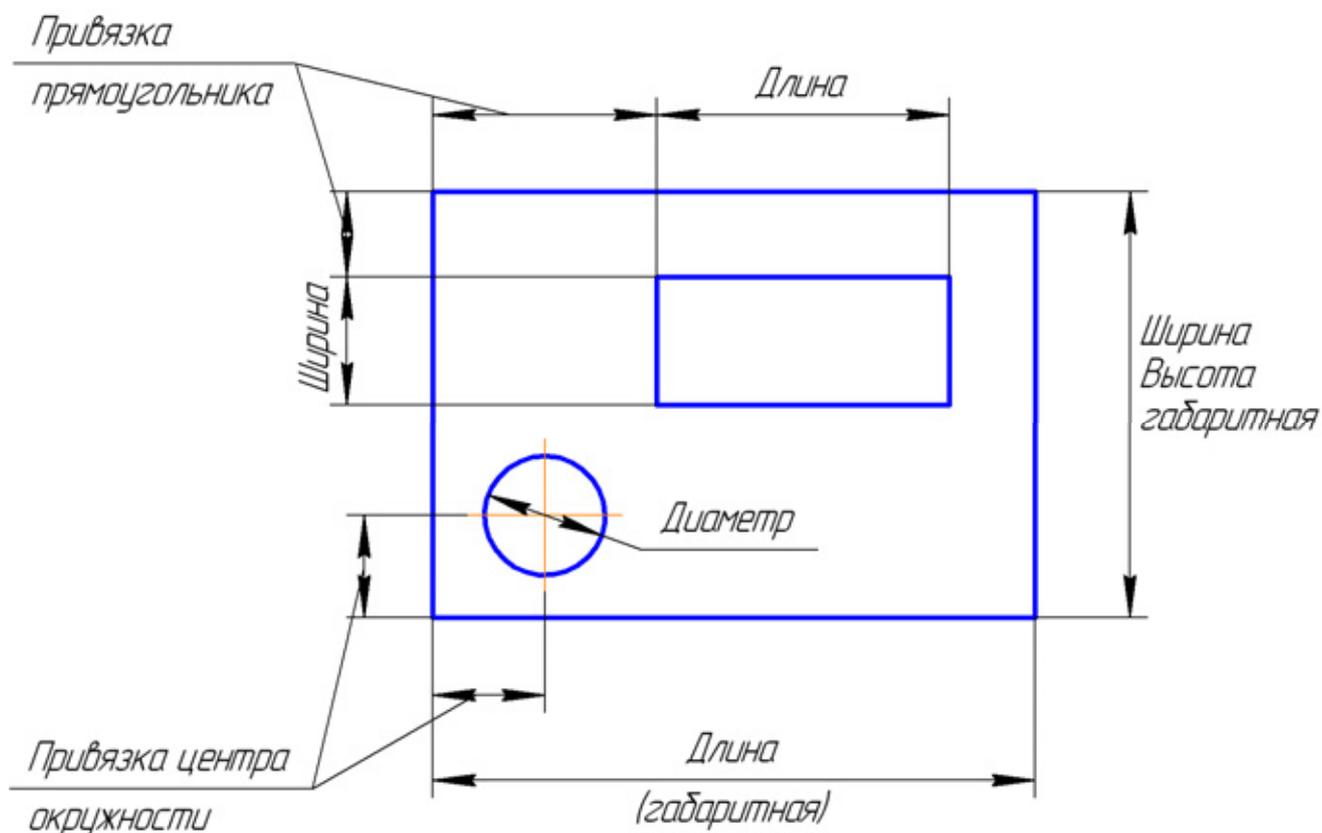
Нанесение габаритных размеров и привязка отверстий
